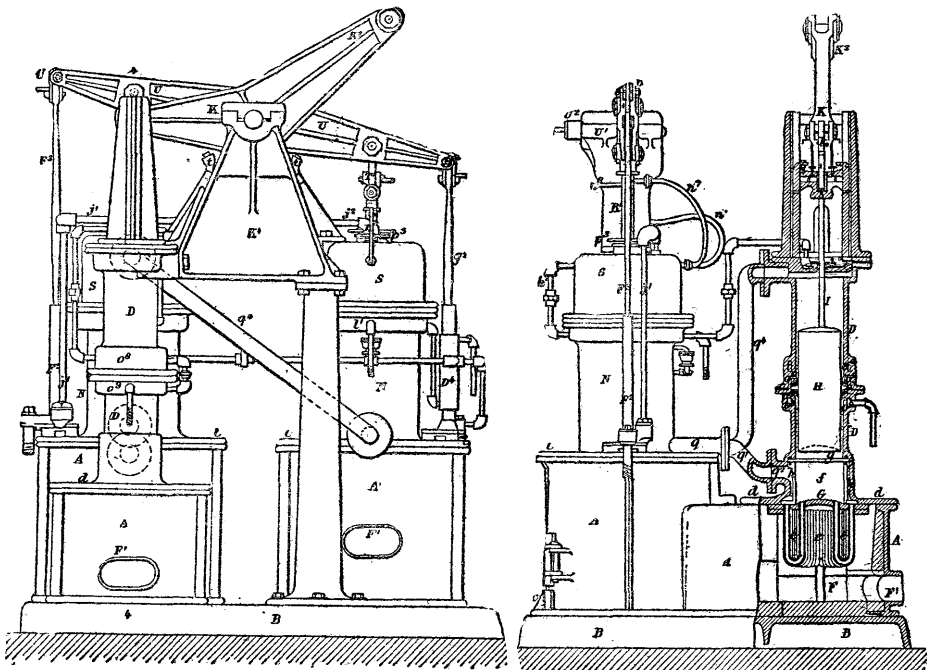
et 59. — Moteur Woodbury. — Variante. — Elévation, vue du côté du cylindre moteur et vue par bout avec coupe par le cylindre moteur. Cette machine comprend deux cylindres déplaceurs N et un seul cylindre moteur D, à double effet. Le haut du cylindre moteur communique avec le bas du déplaceur de droite par le tuyau q_1 , et le bas avec celui de gauche par q . Même légende que pour les figures 39, etc.
